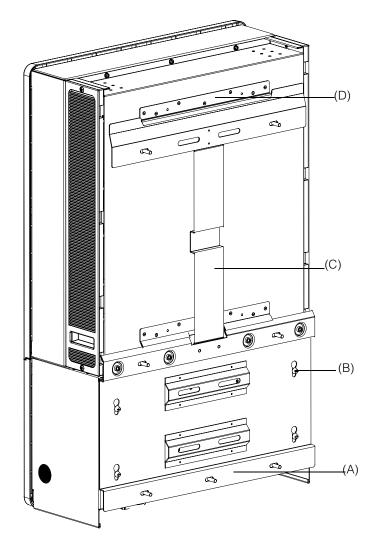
Vue arrière de l'onduleur équipé de son support de montage
